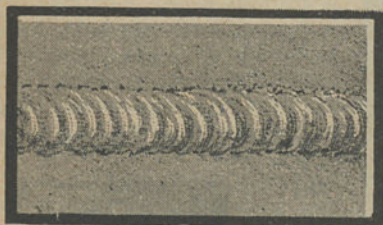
Soldadura de chapa de cobre de 3 m/m (tamanho natural).
